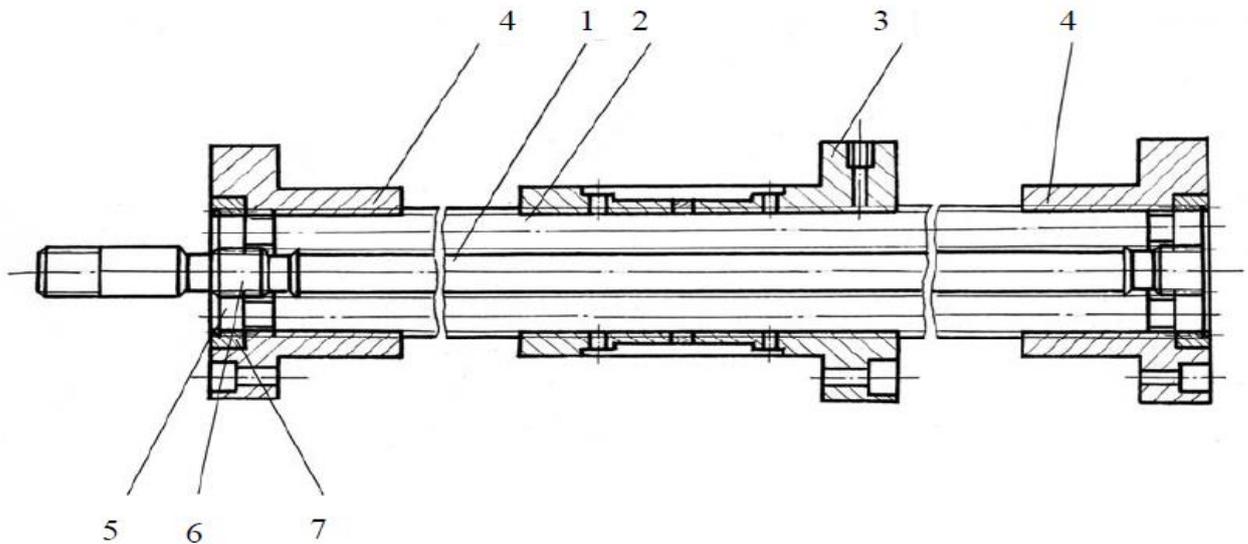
Планетарная передача с длинными резьбовыми роликами и опорными гайками
